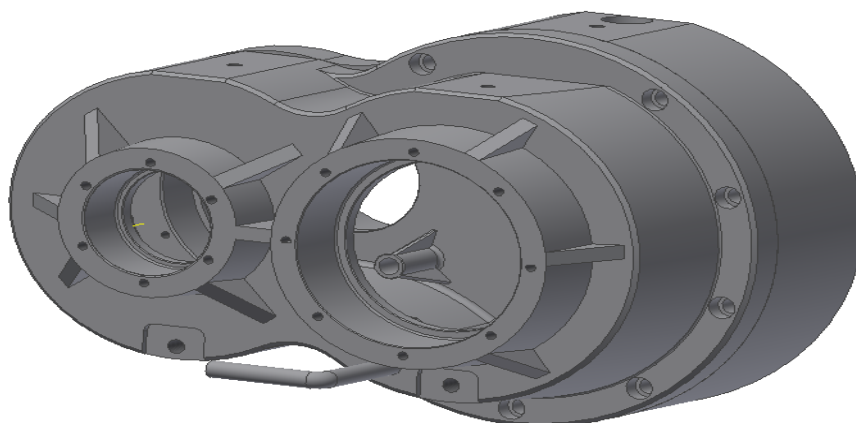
3D model sestavy integrované mechanického převodu s řadícím mechanismem
